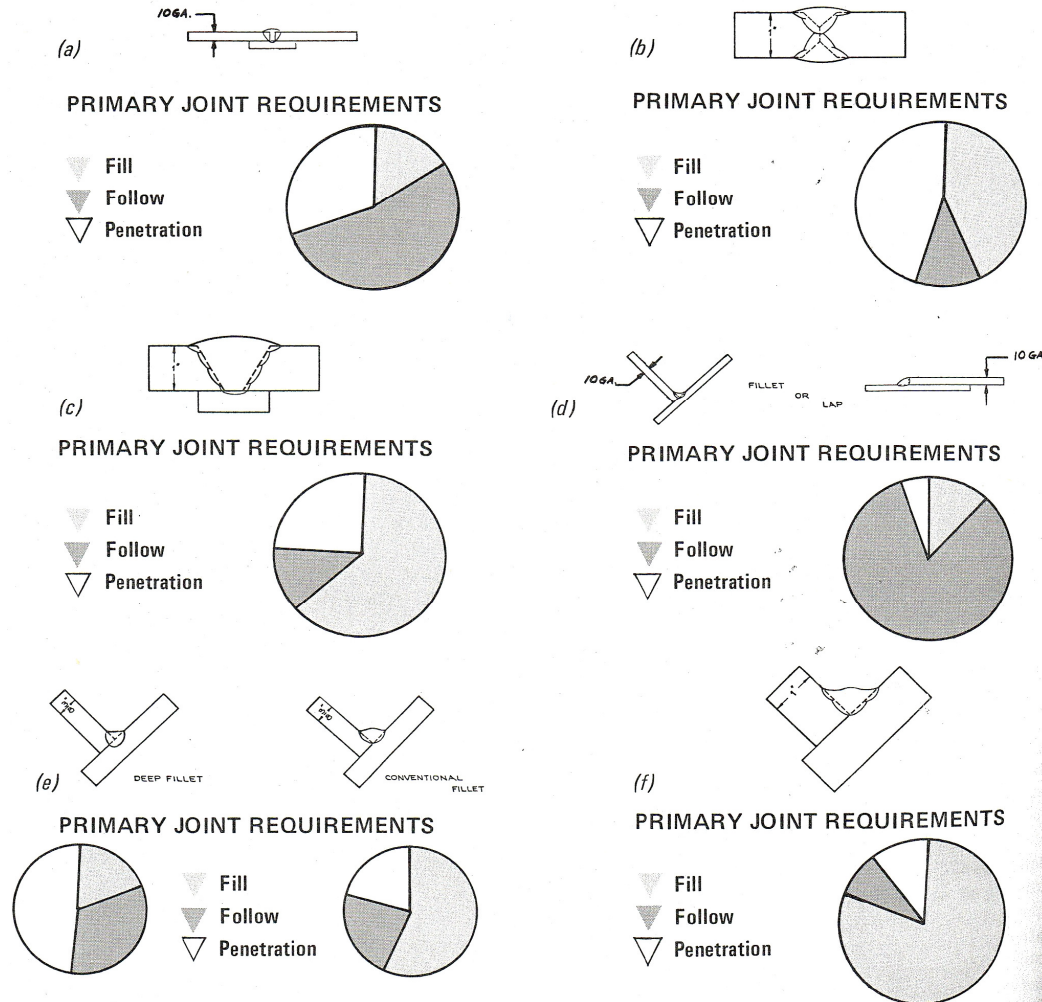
Necessidades em função do tipo de junta de soldadura
